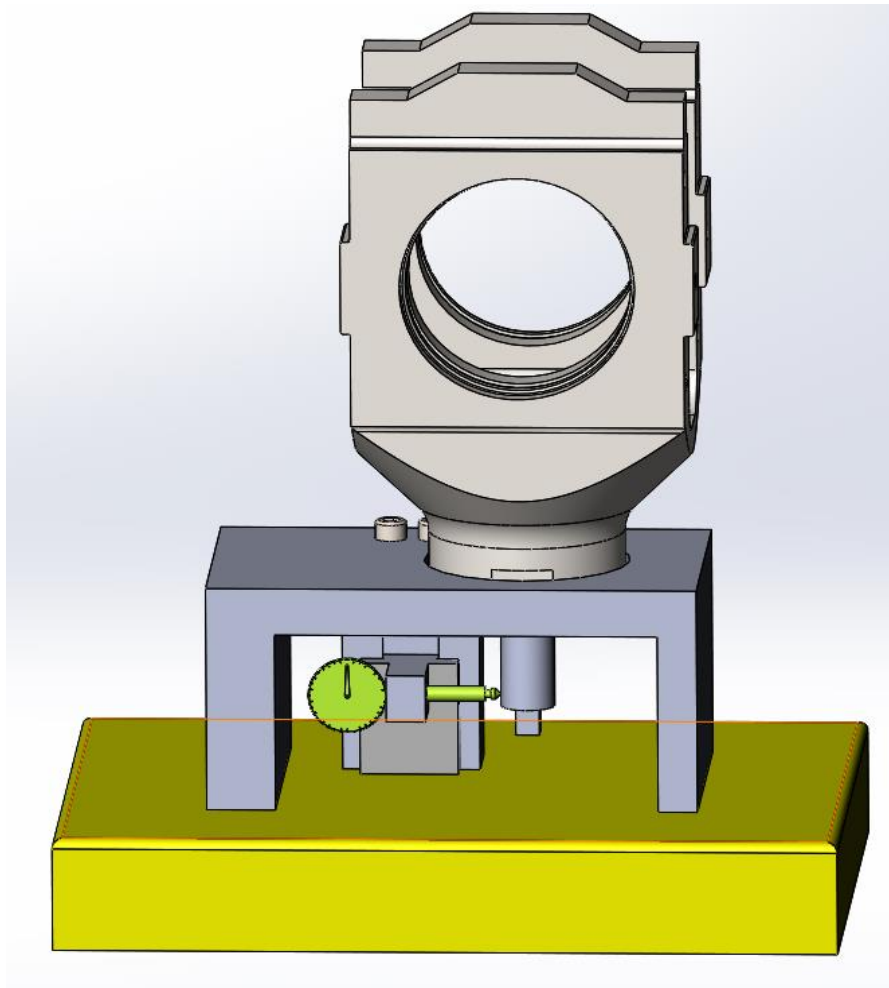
Розроблений контрольно-вимірювальний пристрій із деталлю
